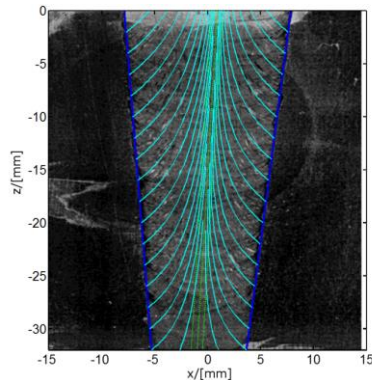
Schlibbild einer austenitischen Schweißnaht mit Schweißnahtmodell
